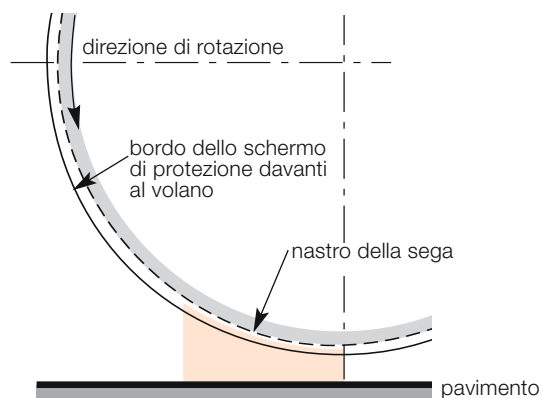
un blocchetto neutralizza la zona di pericolo tra il volano e il pavimento.
